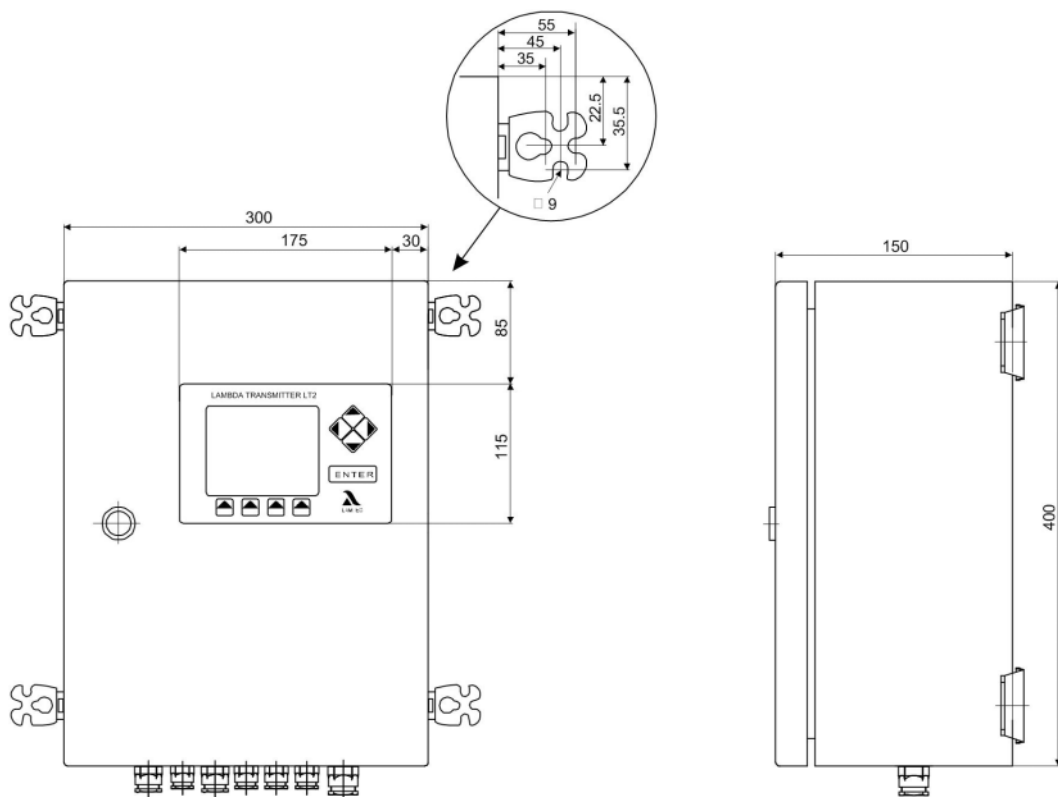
Wandaufbaugehäuse ohne Referenzgaspumpe
